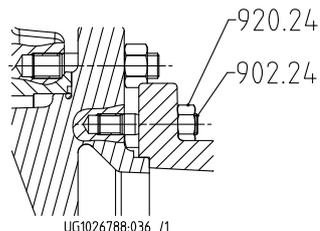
Ausführung mit geschraubten Gehäusedeckel
